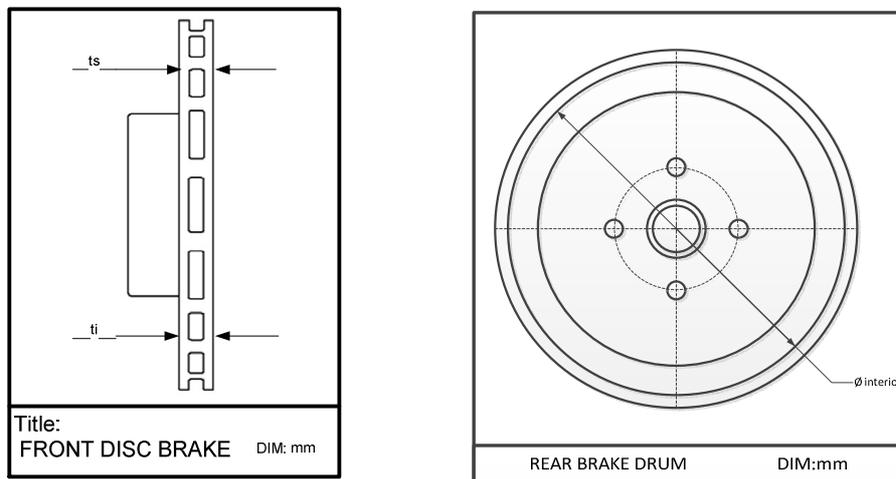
Medida de espesor para disco de frenado delantero, medida de diámetro para tambor de frenado trasero.
